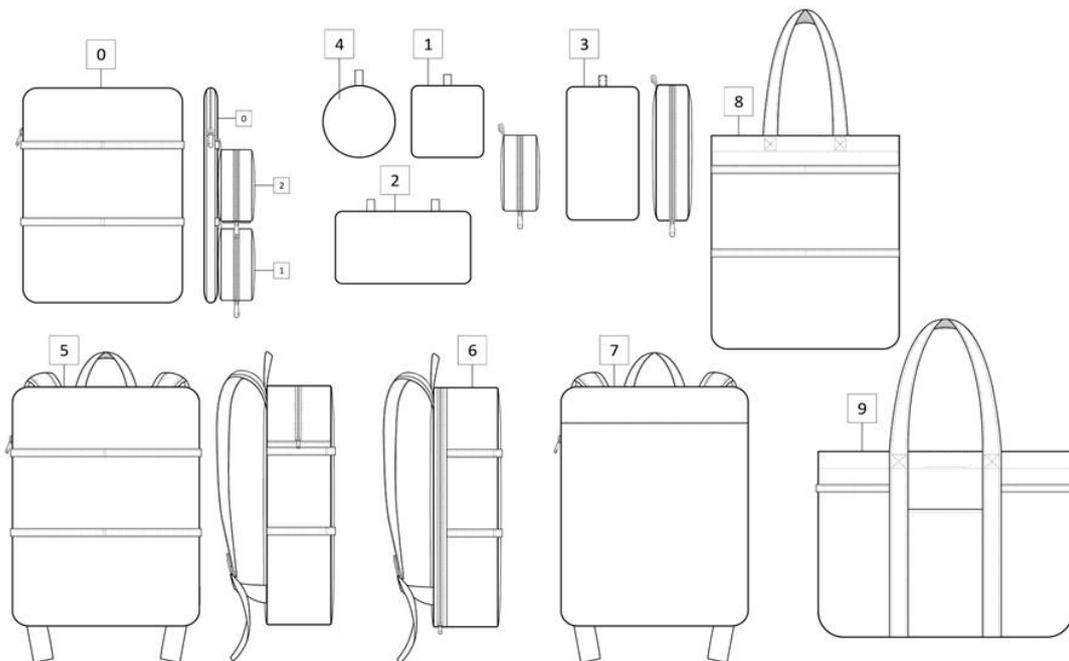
Desenho técnico da coleção industrial (Fonte: Autor)
